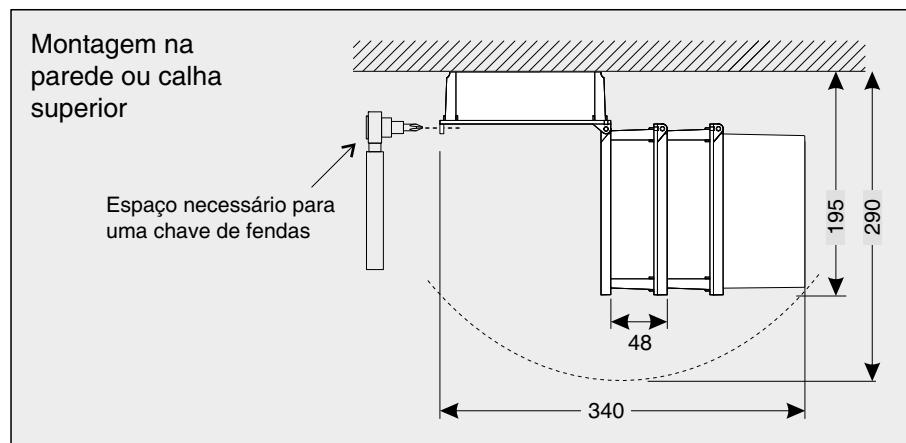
Espaço necessário para a montagem na parede e calha DIN: (dimensões em mm)
